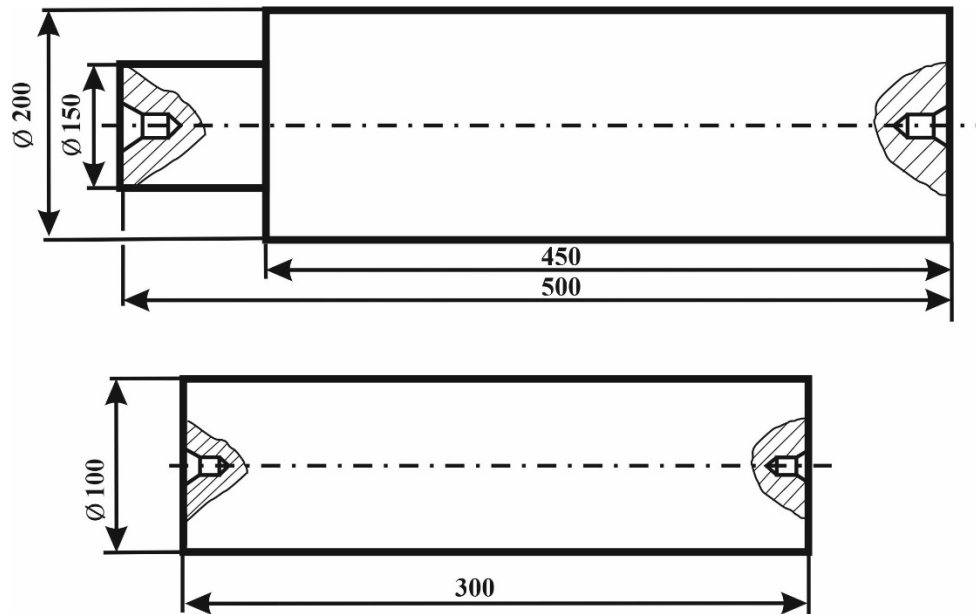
Эскизы образцов для лабораторных испытаний
